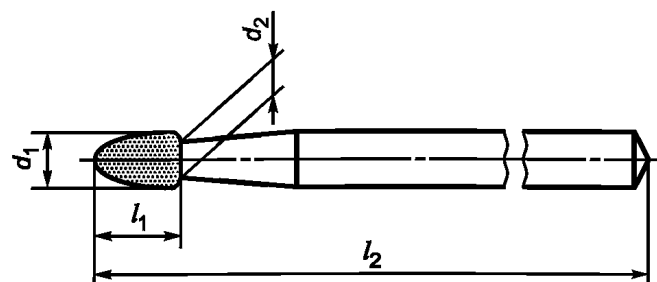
Цилиндрическая с огивальным концом рабочая часть с длиной головки 5,0 мм
